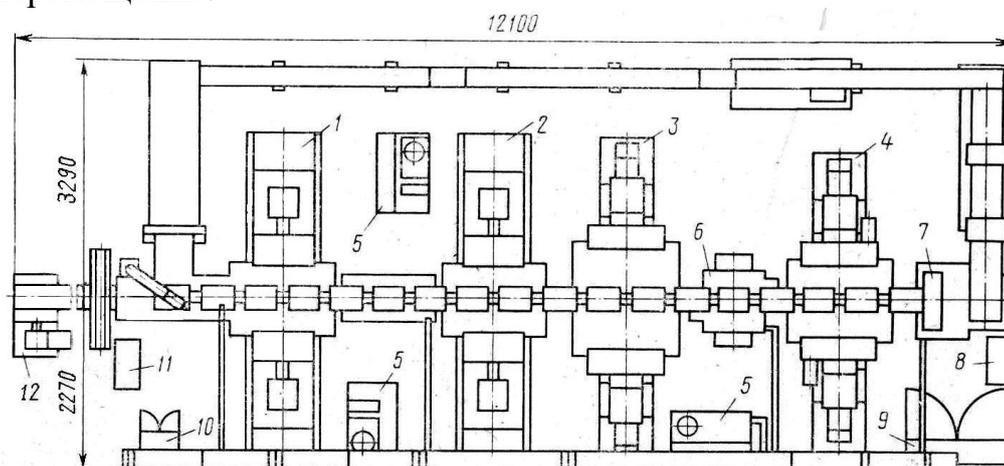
Автоматическая линия с транспортером для возврата приспособлений-спутников, расположенным сбоку на уровне основного транспортера: 1-4 – станки линии; 5 – гидростанция; 6 – контрольно-измерительный автомат; 7 – агрегат для удаления стружки из детали; 8- командоаппарат; 9 – электрошкаф; 10 – центральный пульт управления линией; 11 – инструментальный шкаф; 12 – привод транспортера уборки стружки.
